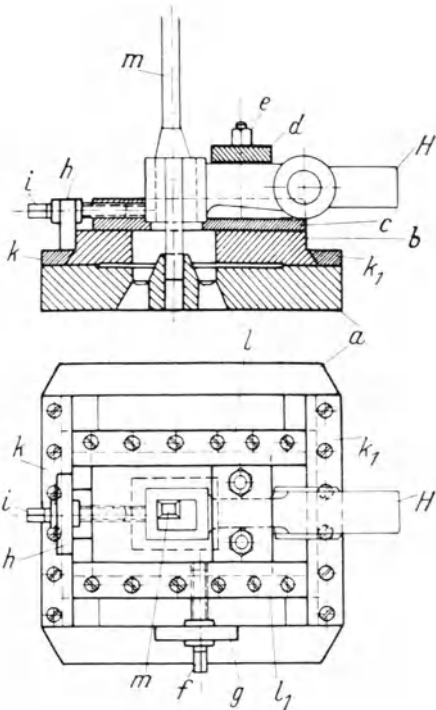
Stoßvorrichtung für Vierkantlöcher in Hebelaugen.
